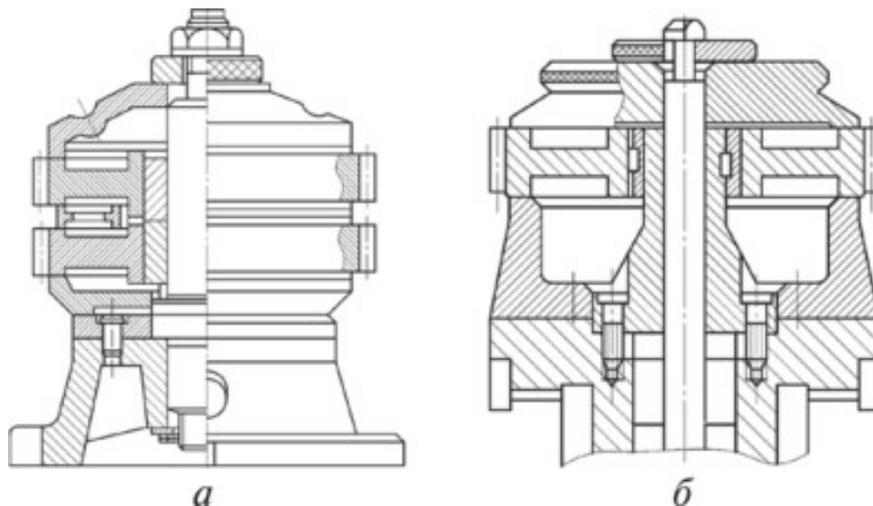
Схемы установки заготовок зубчатых колес при зубофрезеровании: а — двух колес, б — одного колеса
